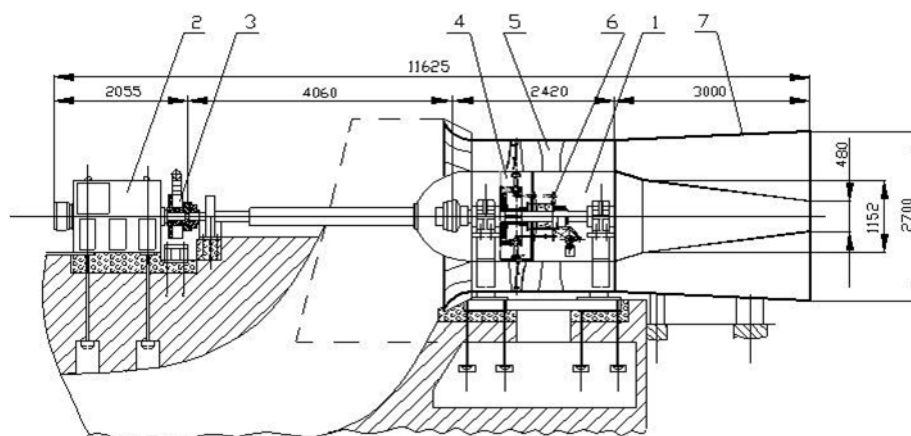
Реверсивный вентиляторный агрегат ВО-24К со сменными и поворотными на ходу лопатками рабочего колеса: 1 – вентилятор ВО-24К; 2 – синхронный электродвигатель 630кВт, 750 об/мин, 6,0 кВ; 3 – электромагнитный тормоз; 4 – рабочее колесо с поворотными на ходу сдвоенными листовыми лопатками; 5 – неповоротные лопатки спрямляющего аппарата; 6 – механизм одновременного поворота лопаток рабочего колеса; 7 –
